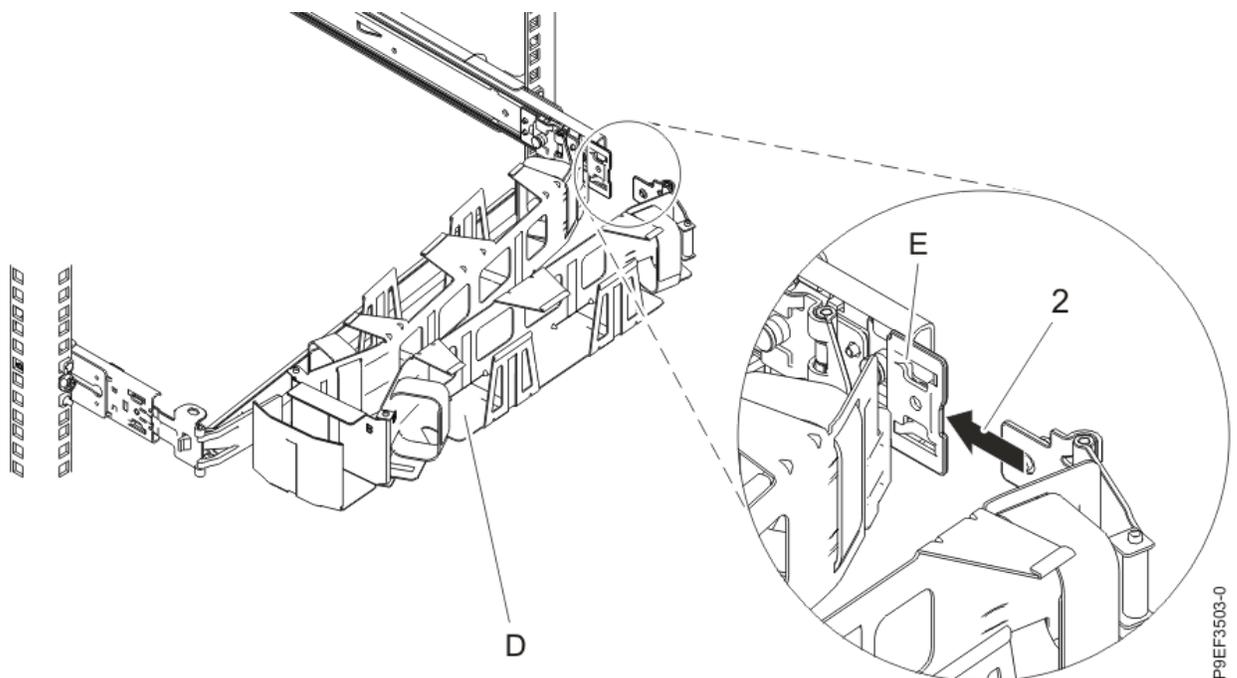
Faites glisser l'autre taquet du bras de routage des câbles dans le logement du support d'extension
